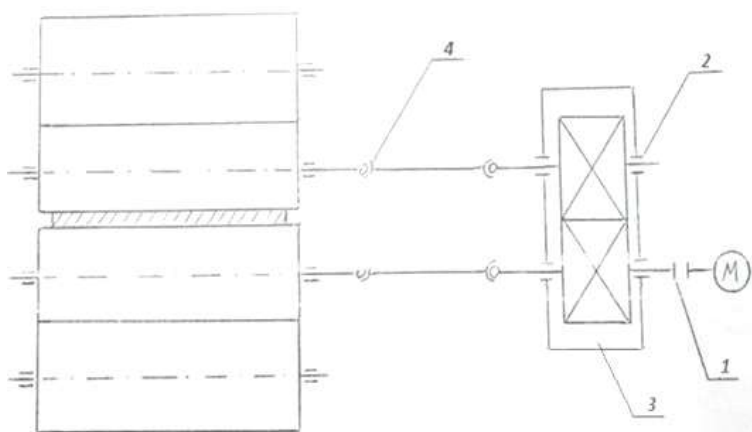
Пример схема смазывания привода чистовой клетки стана 2000 горячей прокатки
